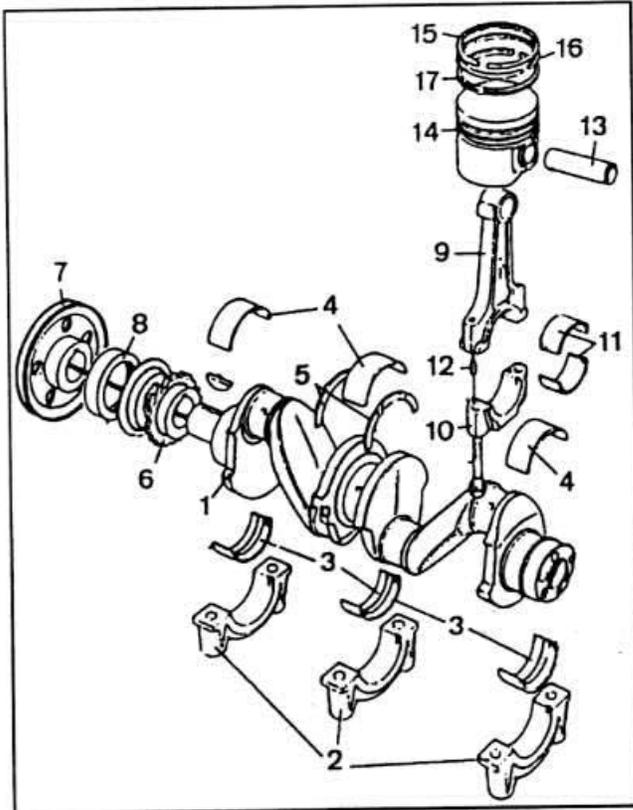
D.58. Кривошипно-шатунный механизм двигателя HCS.
